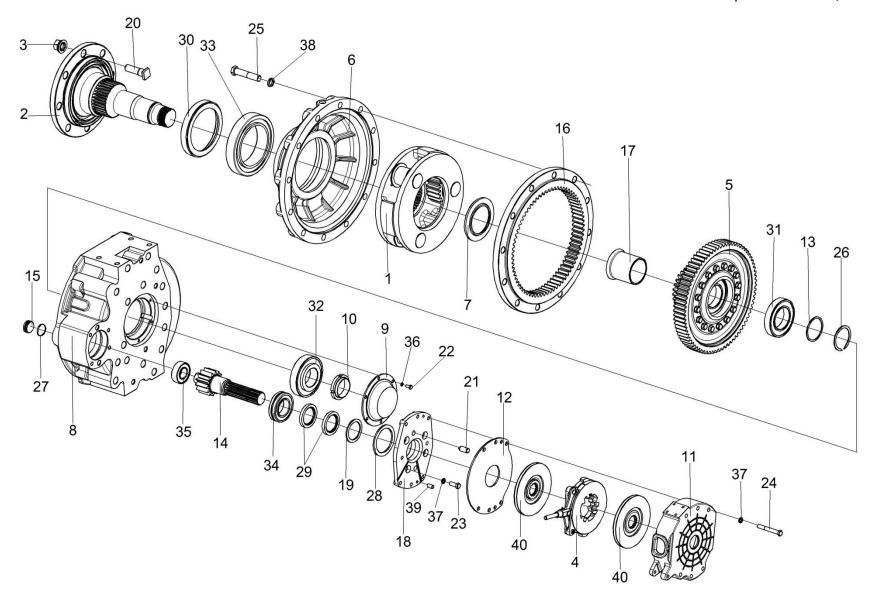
Редуктор бортовой КЗК-10-0107200 (лист 2)
